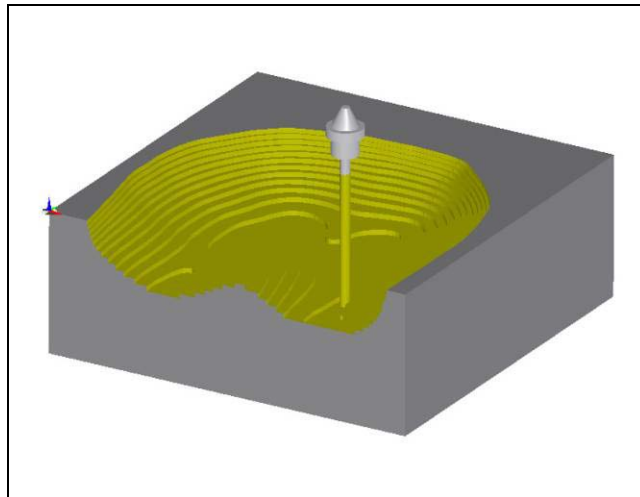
Simulação da Usinagem CNC de um assento no software Edgecam.
